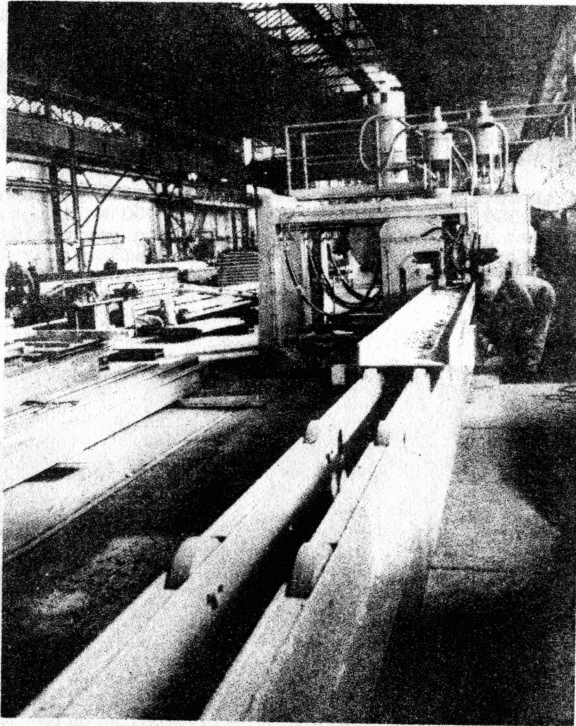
Blechträgerdurchlaufschweißanlage,
